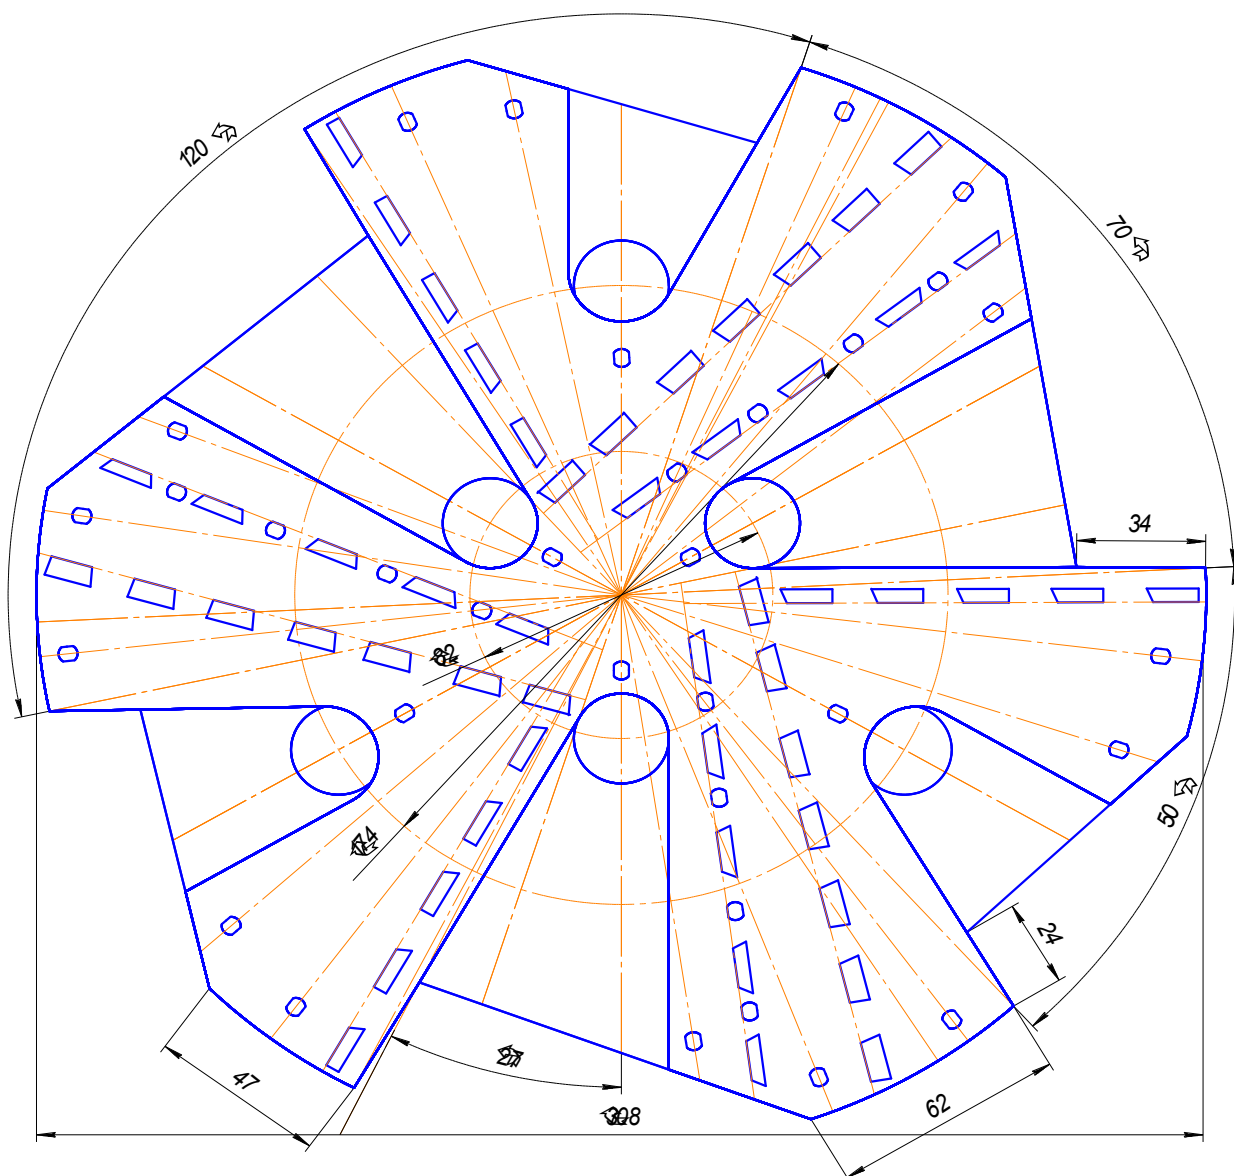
Запропонована схема армування вибійного стираючо-ріжучого фрезера ФЗ-308 з новою конфігурацією пластин
